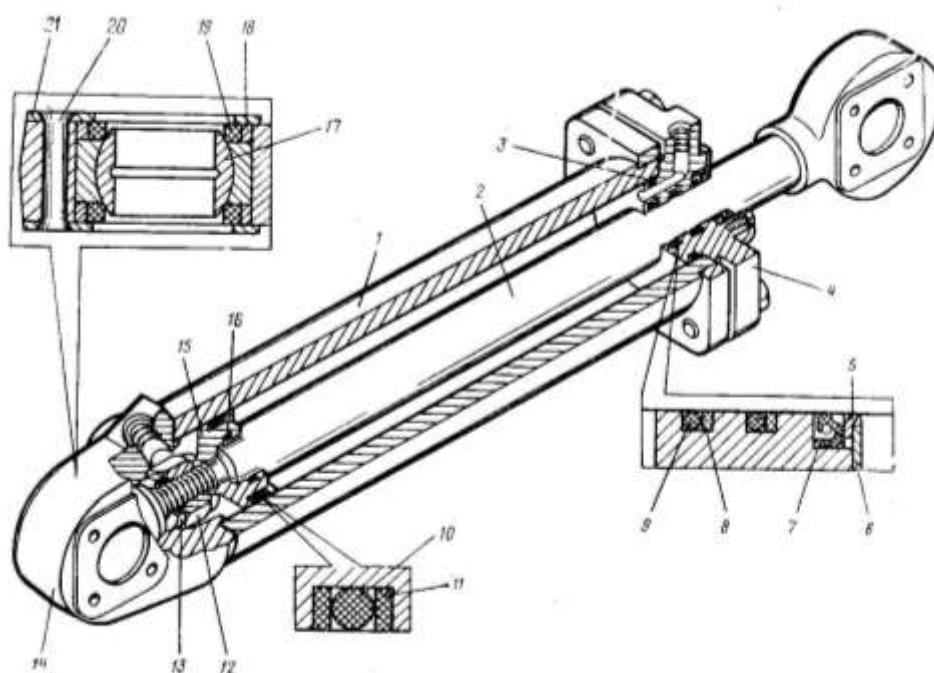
Гидроцилиндр: 1 – корпус; 2 – шток; 3, 9, 10, 16, 19 – кольца уплотнительные; 4 – крышка передняя; 5 – скребок; 6 – крышка; 7 – манжета; 8, 11 – шайбы защитные; 12 – гайка; 13 – кольцо конtringящее; 14 – крышка задняя; 15 – поршень; 17 – подшипник; 18 – кольцо; 20 – заклепка; 21 – пластина
